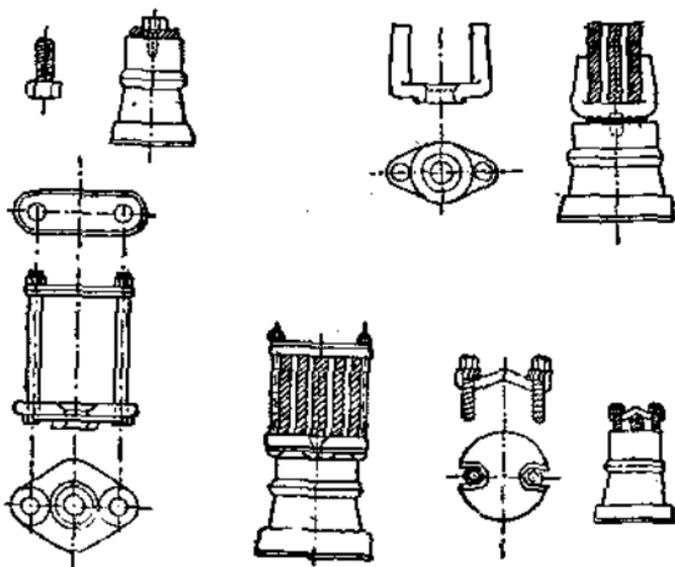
Арматура для крепления шнв на опорных изоляторах.
